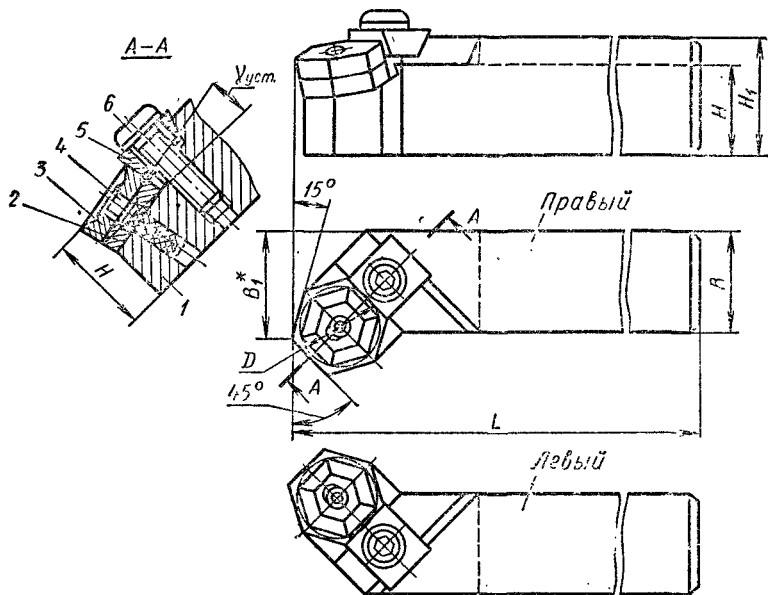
Схема установки многогранной пластинки в корпусе резца
